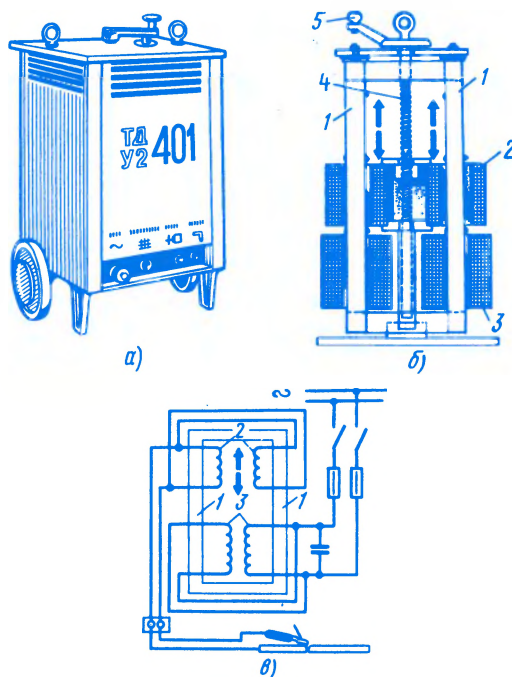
Сварочный трансформатор ТД-401У2: а — общий вид, б — вид без кожуха, в — электрическая схема
